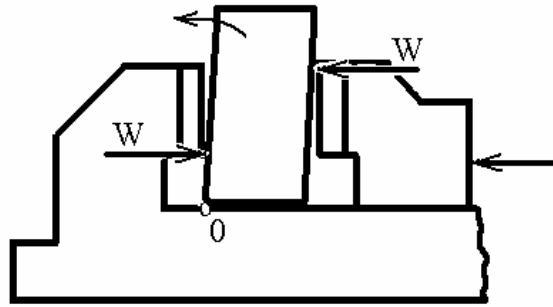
Схема утворення похибки закріплення під час встановлення заготовки в лещатах
